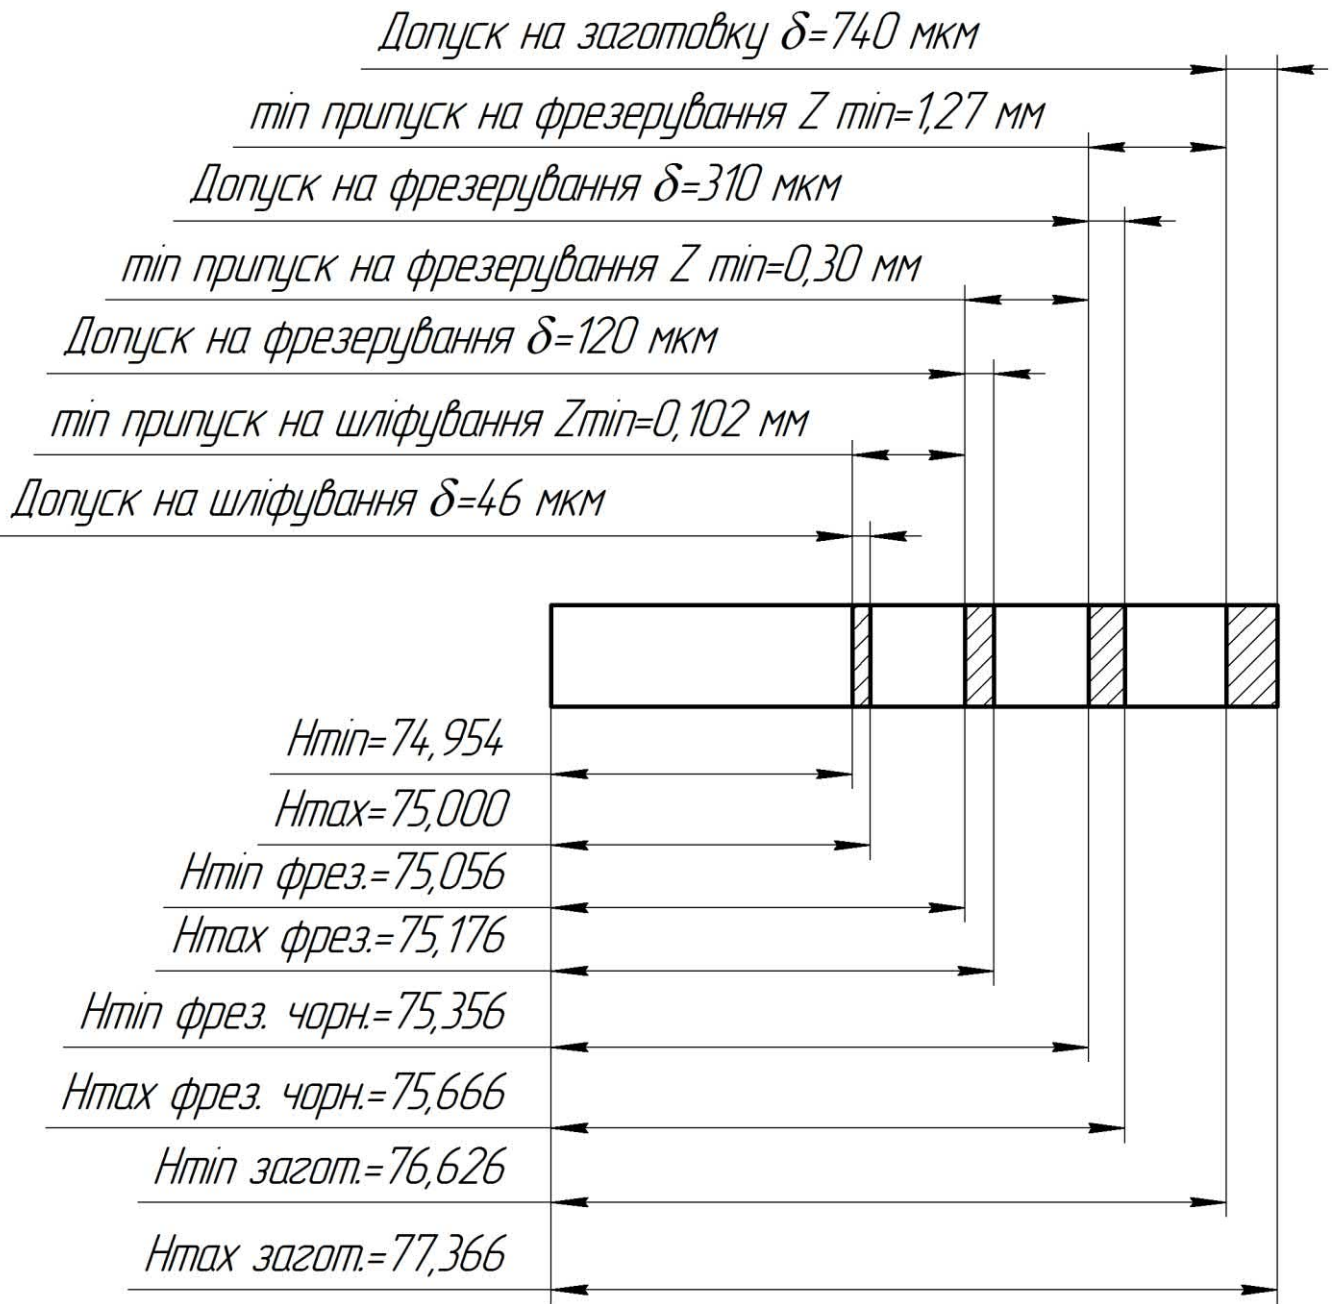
Схема розташування припусків і допусків на механічну обробку поверхні розміром 75h8
